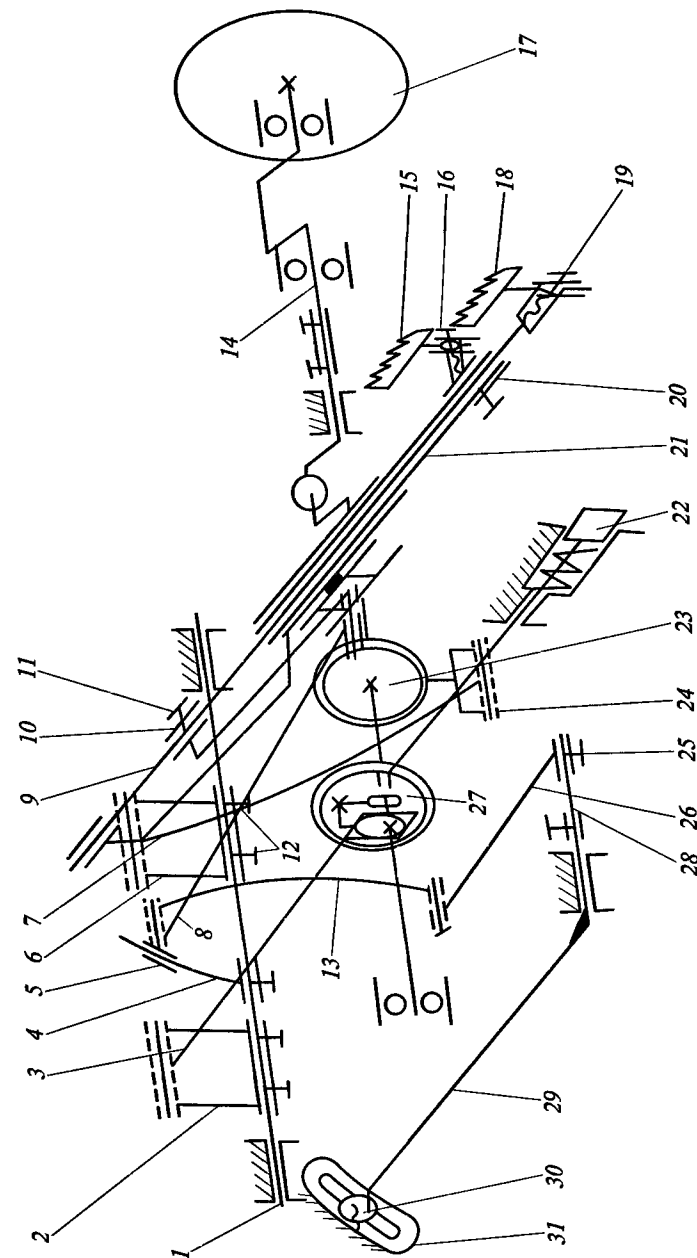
Кинематическая схема механизма перемещения реек швейной машины класса 1276
